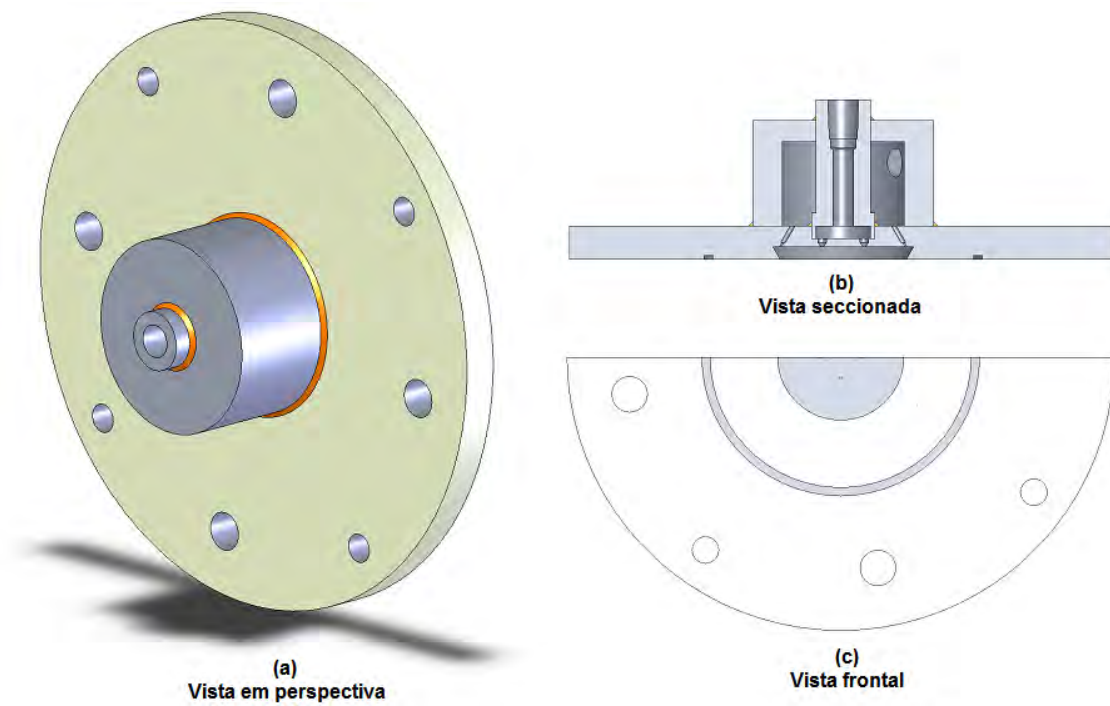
Placa injetora bipropelente (a) Vista em perspectiva; (b) Corte lateral; (c) Vista frontal.
